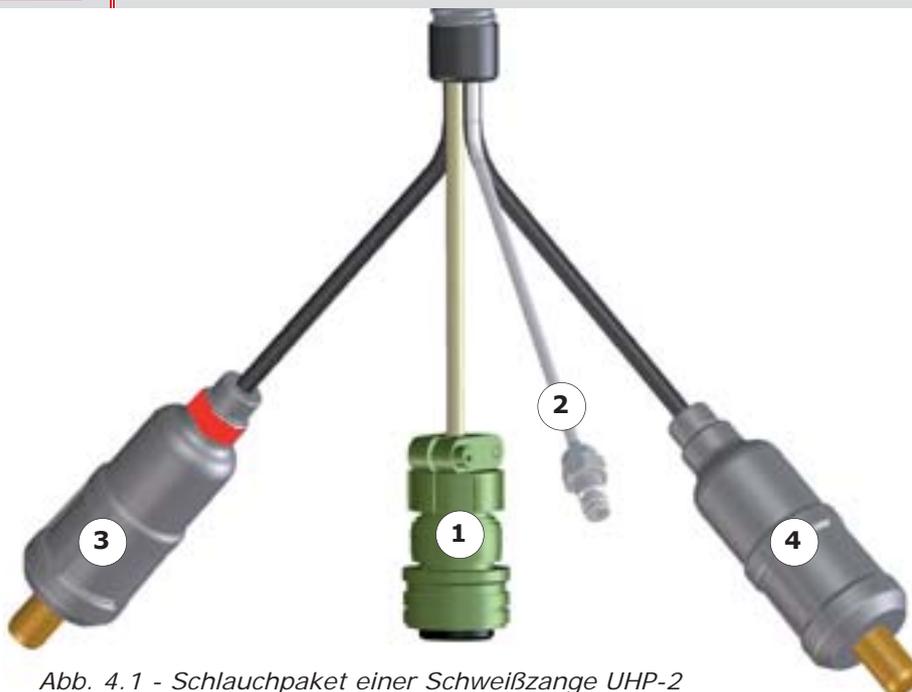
Schlauchpaket einer Schweißzange UHP-2
